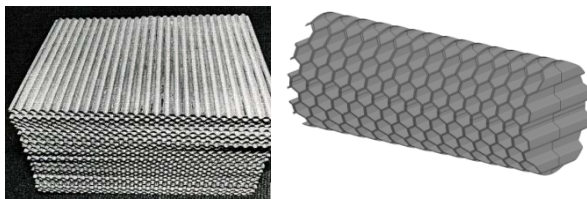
Сотовый блок и образцы сотовых конструкций для динамических испытаний.
